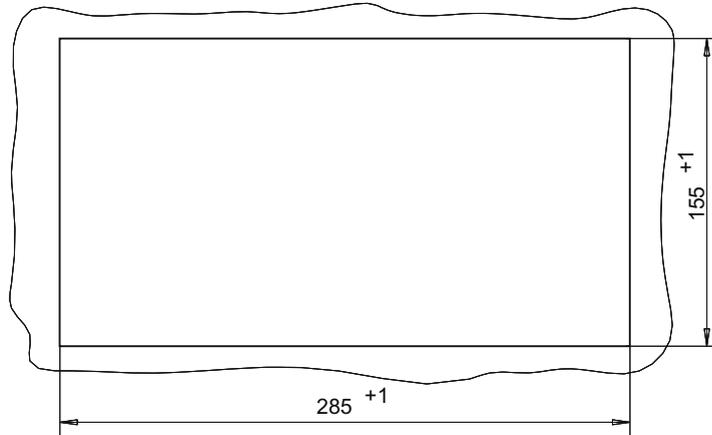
Montageausschnitt für die Maschinensteuertafel MCP 310C PN
